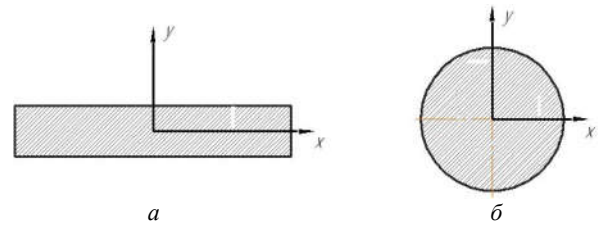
Контур заготовок цилиндрической зубчатой передачи:
